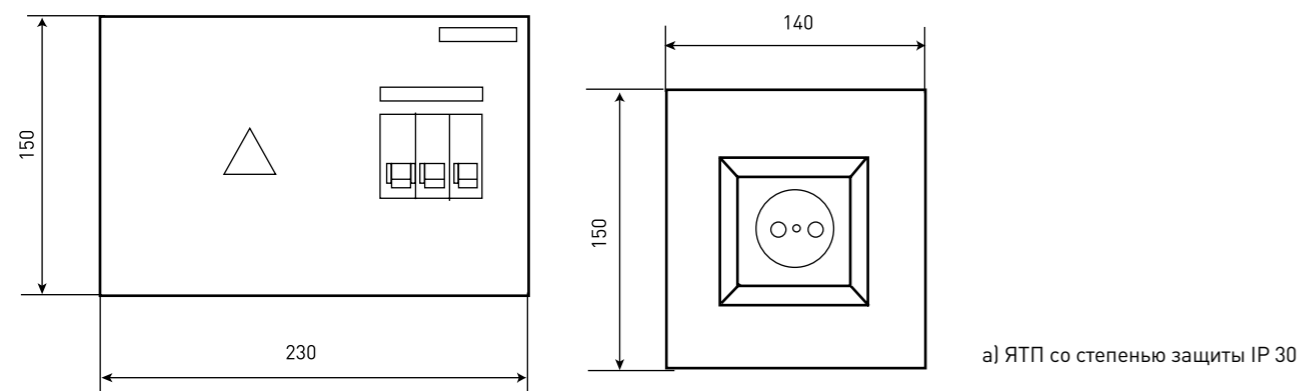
Общий вид и габаритные размеры ящика силового ЯТП
